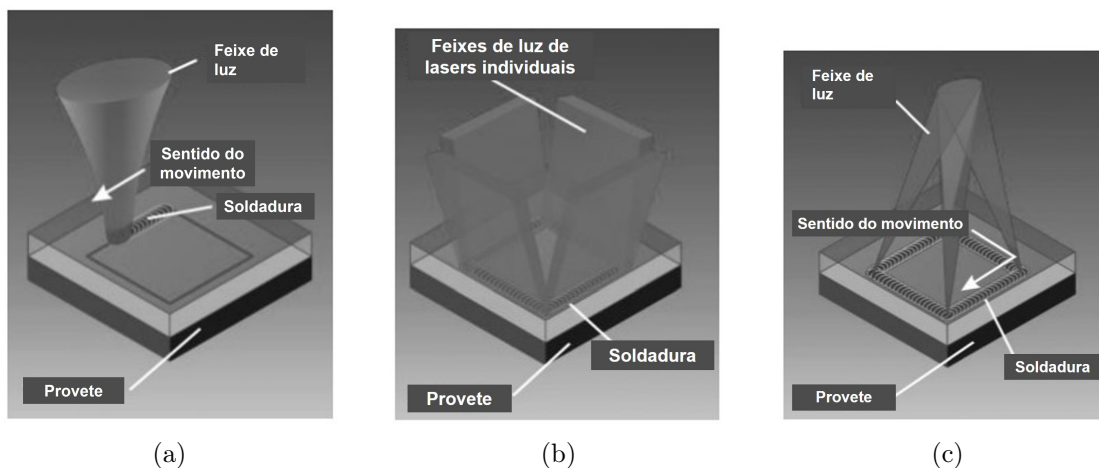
Representação esquemática das técnicas de soldadura por transmissão. a) Soldadura por contorno. b) Soldadura simultânea. c) Soldadura quase simultânea. Adaptado de [13].
